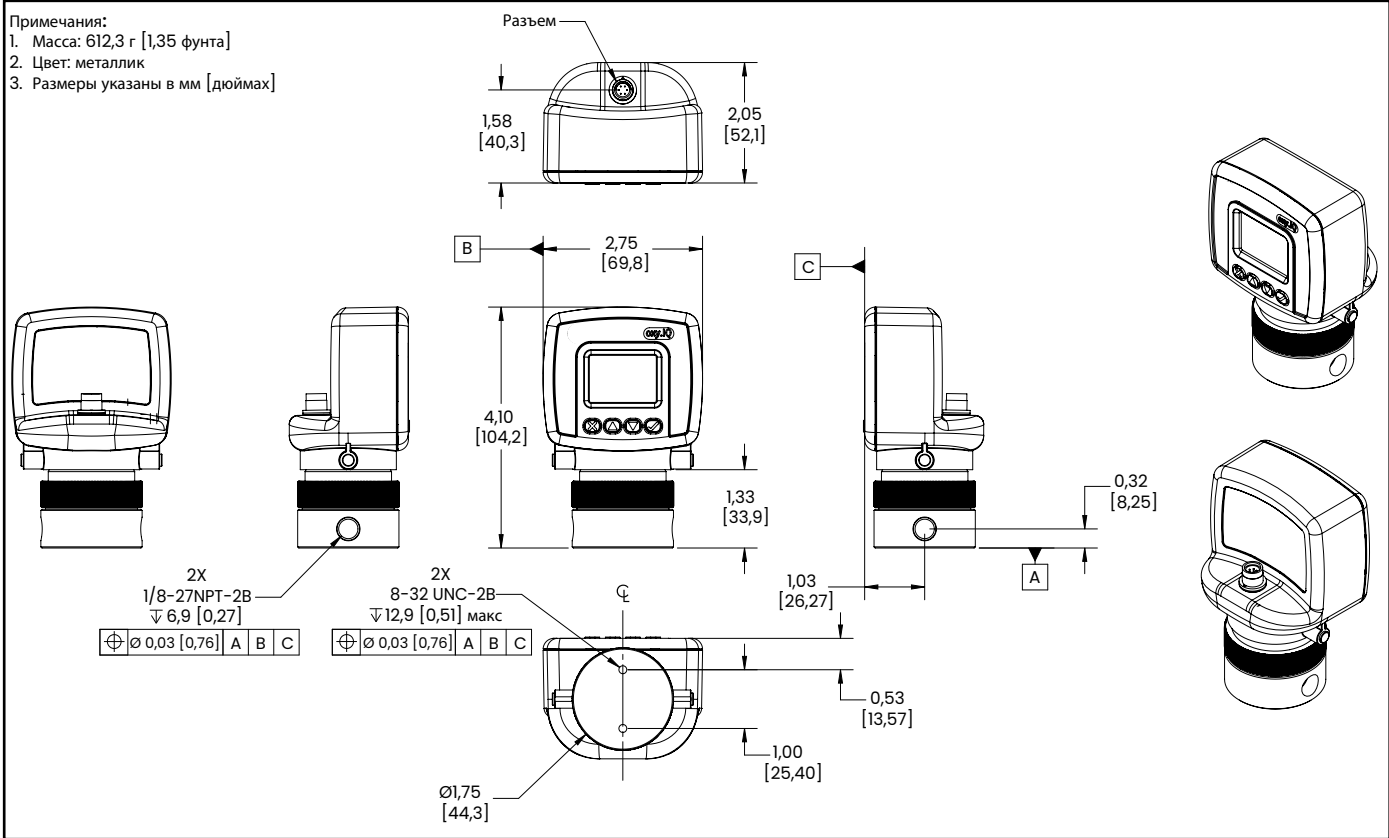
Габаритно-установочный чертеж (№ чертежа 712-1840)
